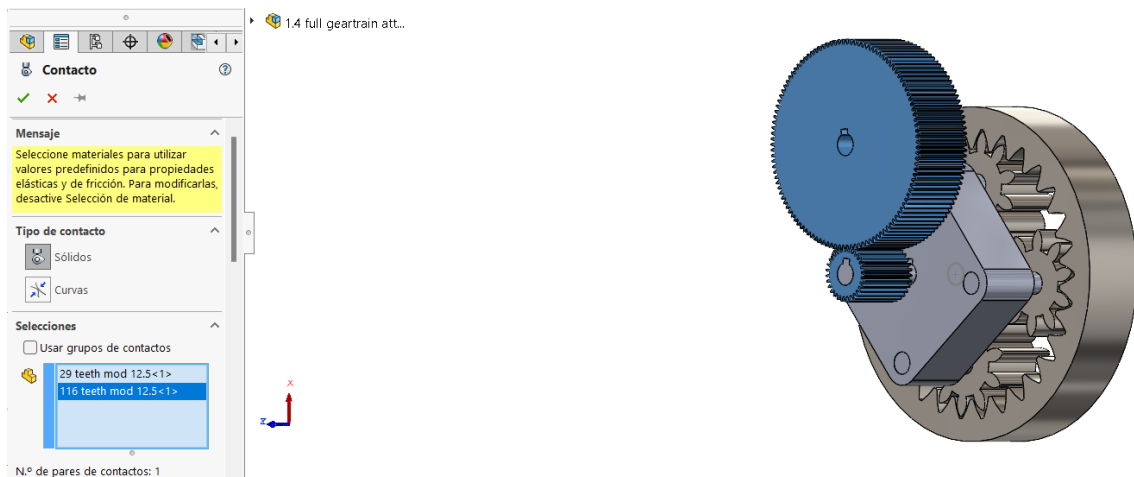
Captura de pantalla enseñando la condición de contacto de la etapa final del segundo sistema de engranajes. Elaboración propia usando SolidWorks.
